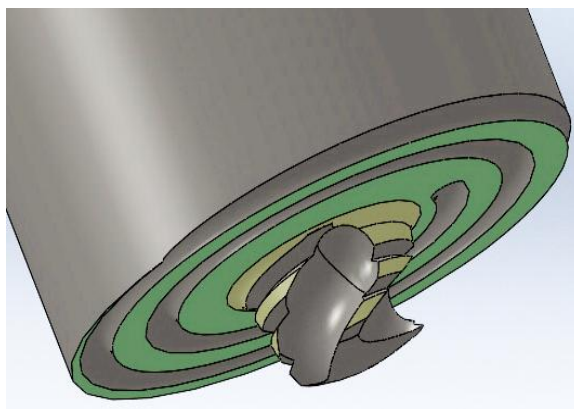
Модель расположения спиральных канавок инструмента для СТП с рабочей частью спиралевидной формы конструкции ОАО «ВНИИАЛМАЗ»
